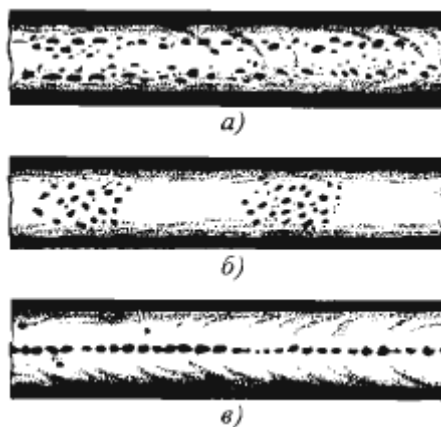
Характер пористости: в наплавленном металле шва: равномерная пористость; скопления пор; цепочки пор.
